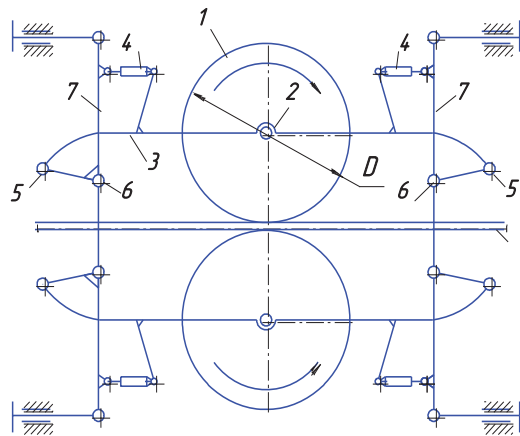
Схема тягового устройства (вид сверху). 1 – ведущие колеса; 3, 7, 4 – система рычагов; 2, 5, 6 – подшипники.
